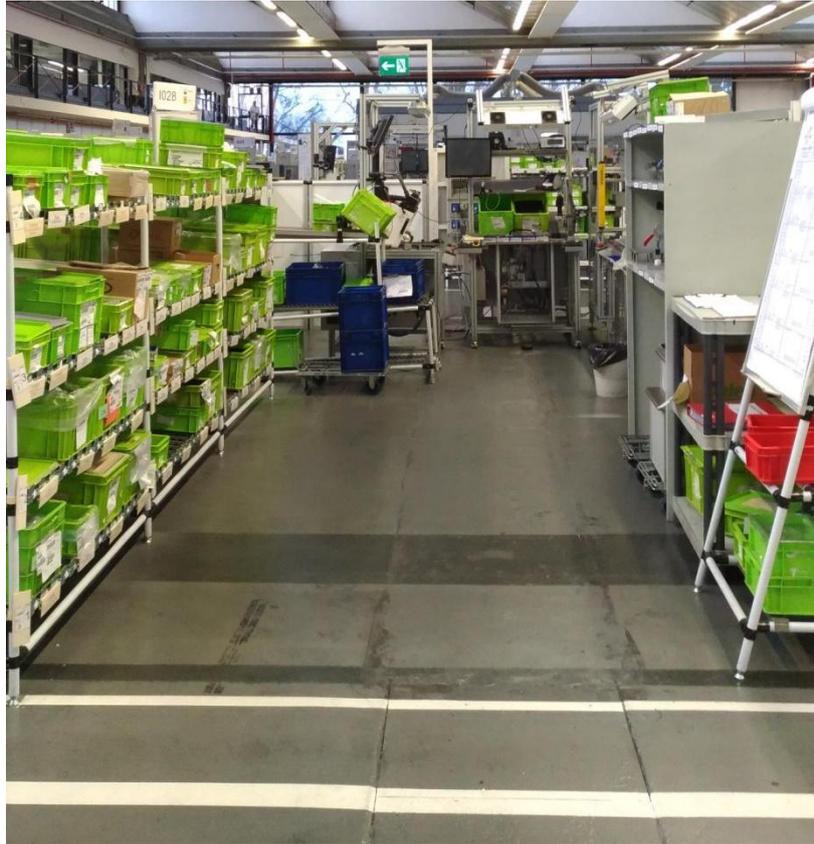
Disposizione finale dell'isola di lavoro I028
